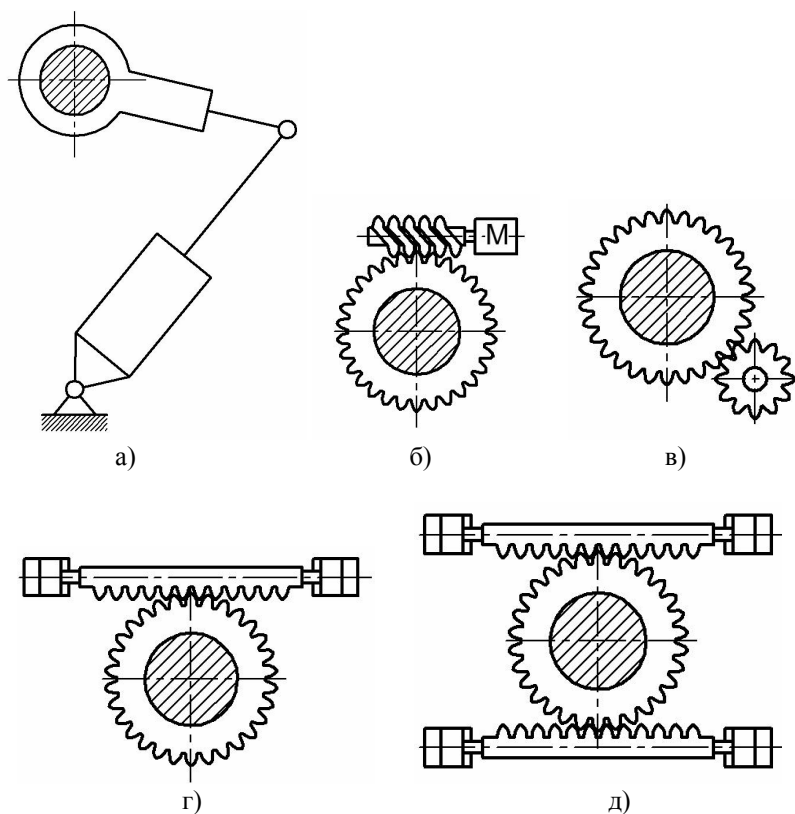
Схеми механізмів повороту опорно-поворотних пристроїв машин маніпуляторного типу
